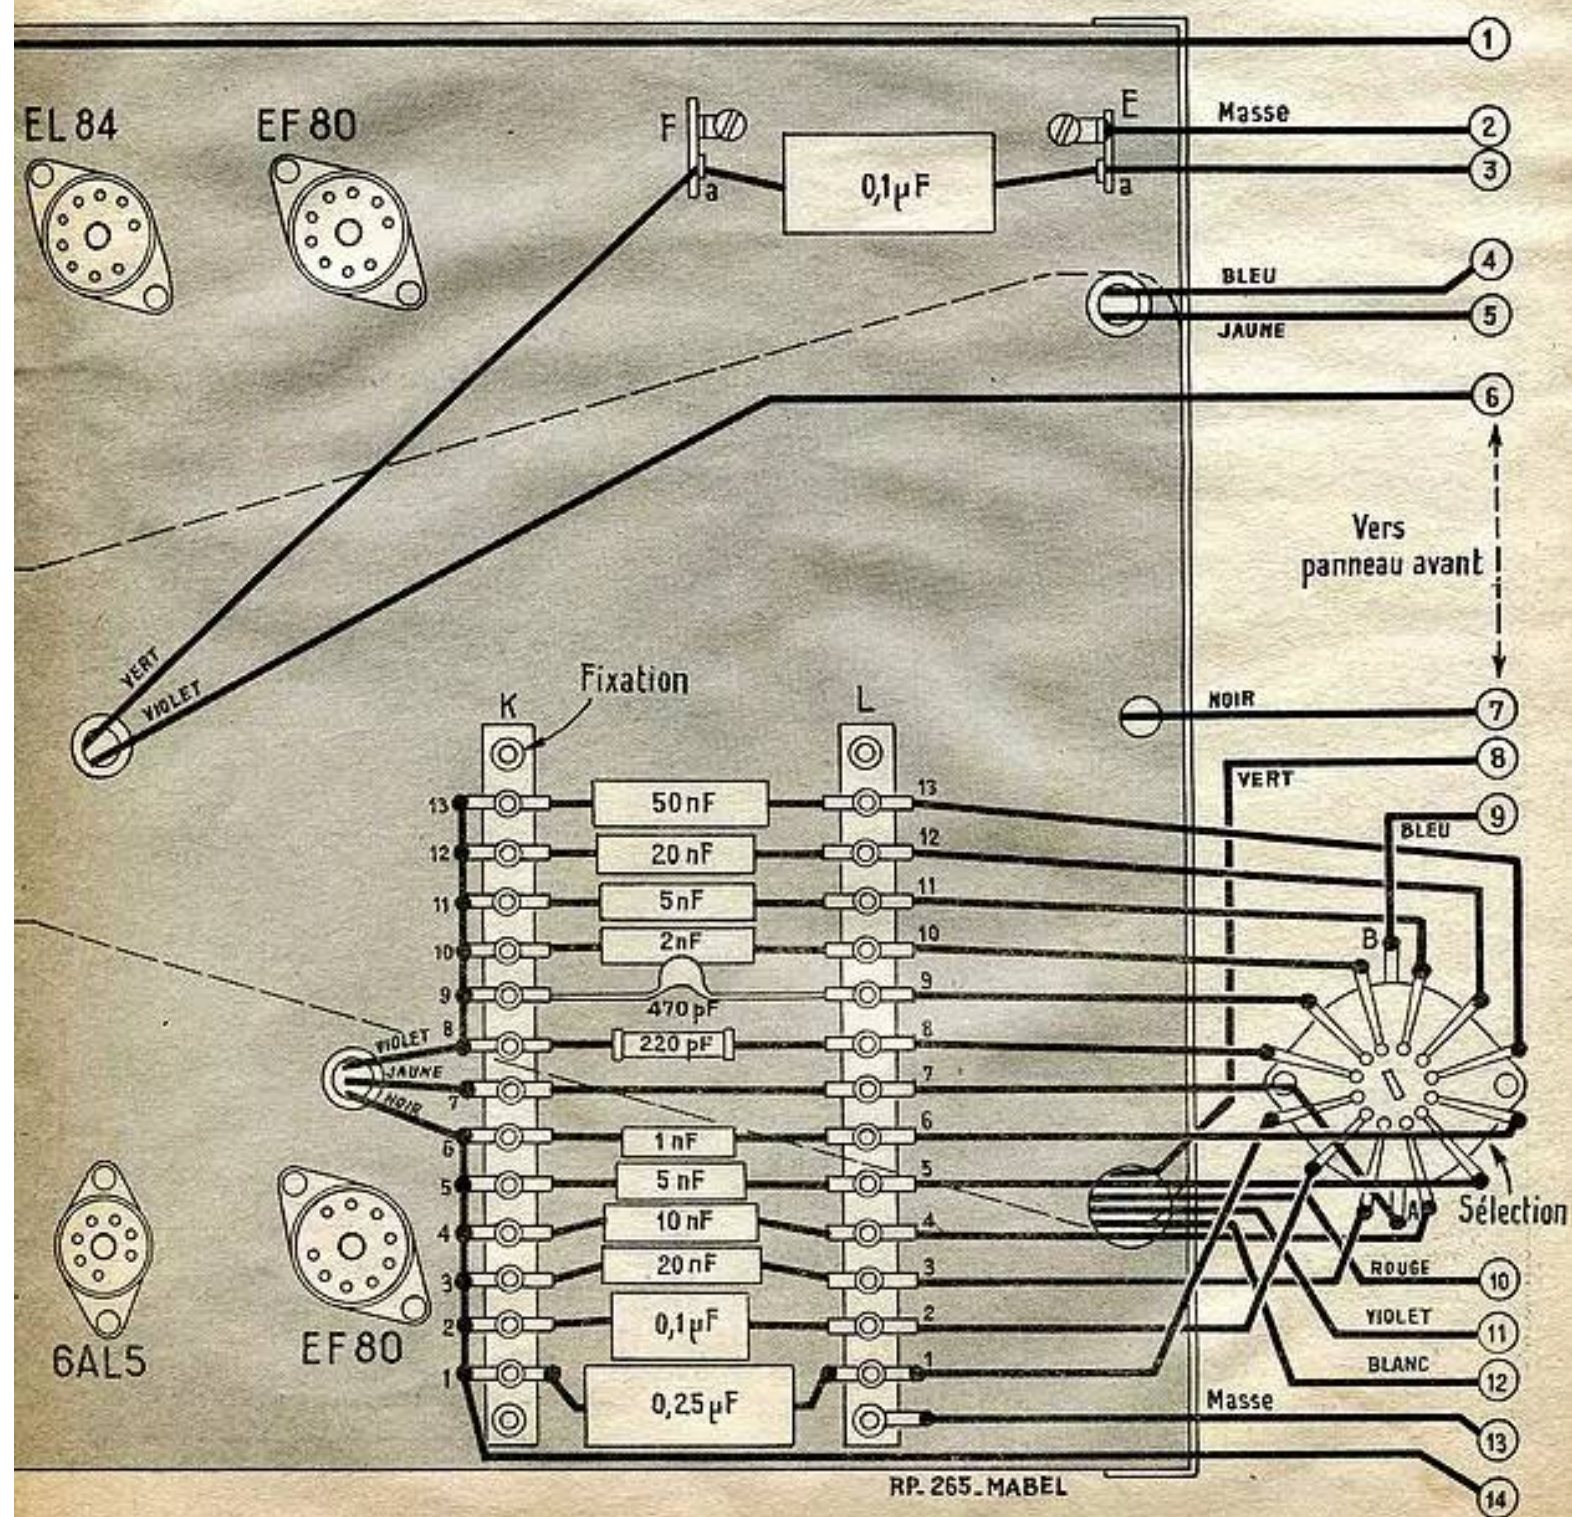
CABLAGE DU CHASSIS HORIZONTAL (DESSUS)
